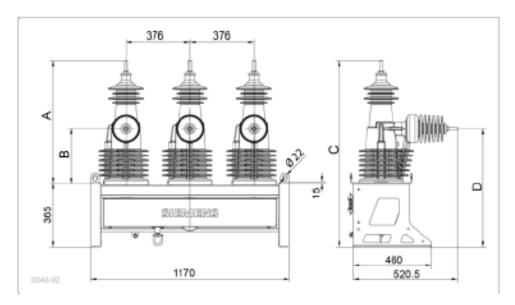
Габаритные размеры 3-фазного блока переключателей Модель 38
